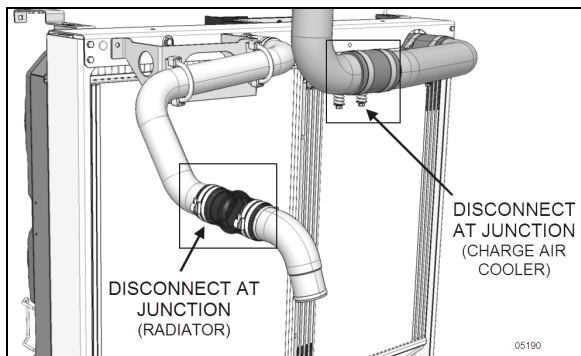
RADIADOR & CONEXIÓN SUPERIOR DEL CAC
